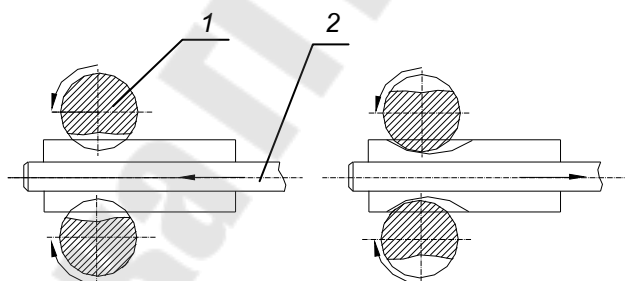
Схема обработки заготовки на пиллигримовом стане:
